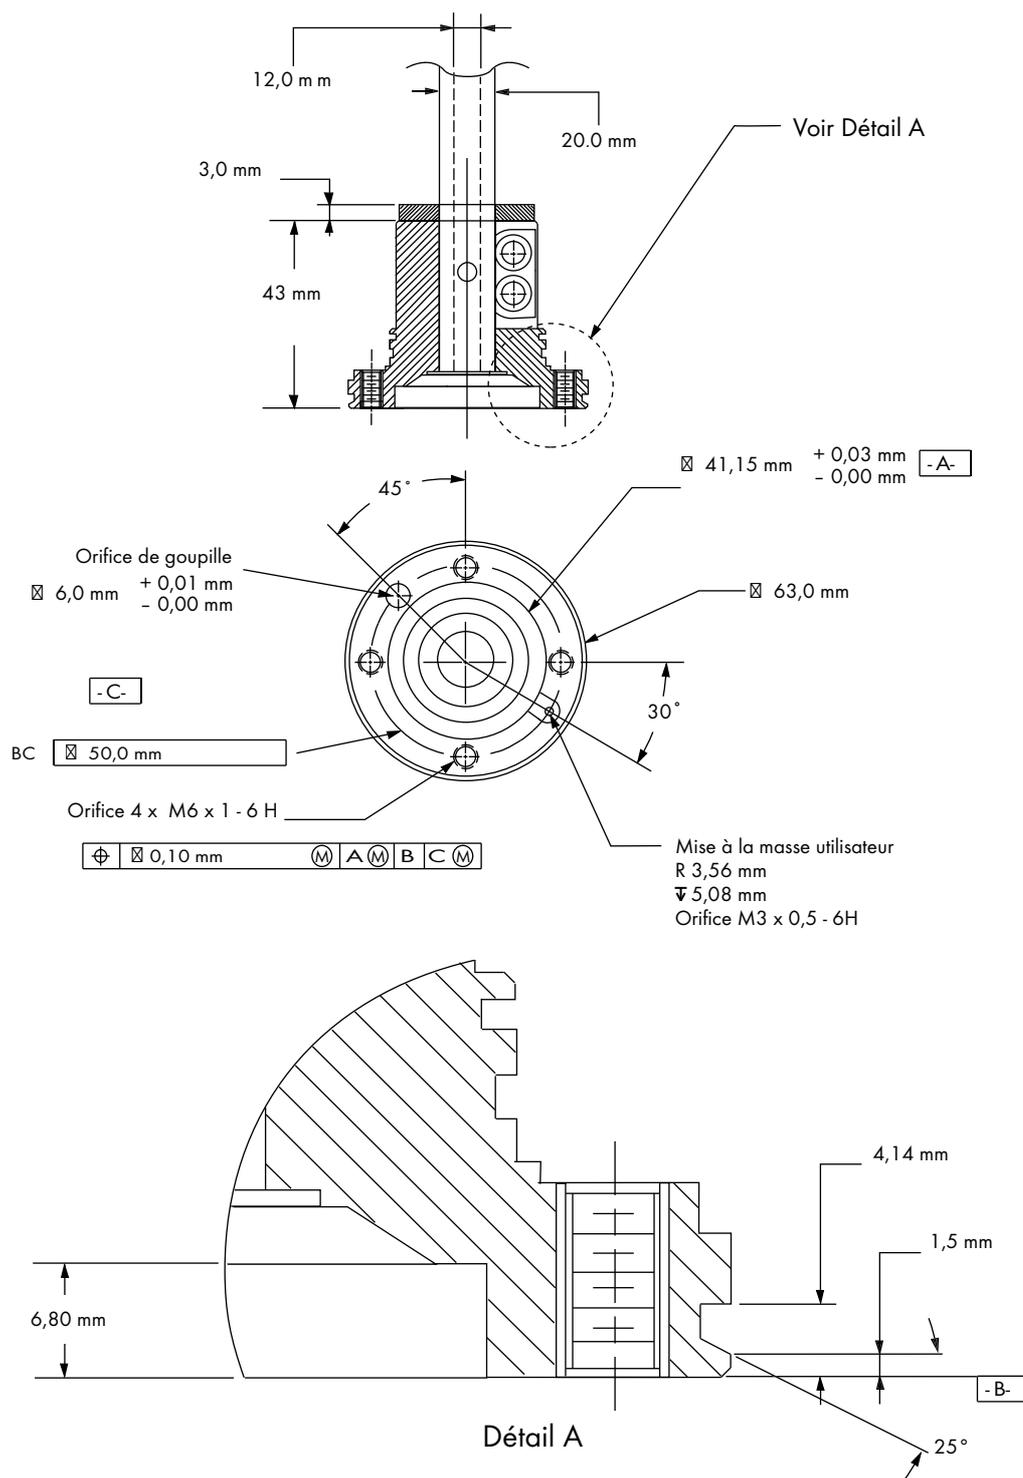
dimensions de la bride outil pour robots Adept Cobra
